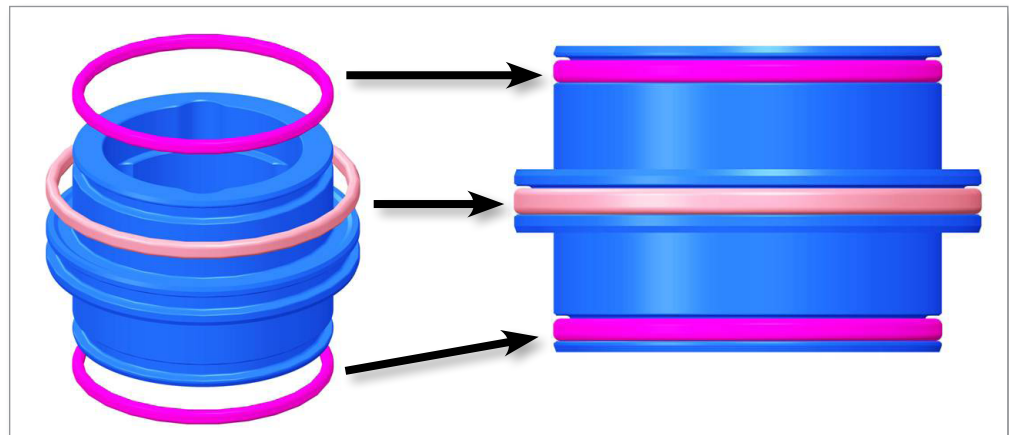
Installation der O-Ringe auf dem Kolbendeckel
